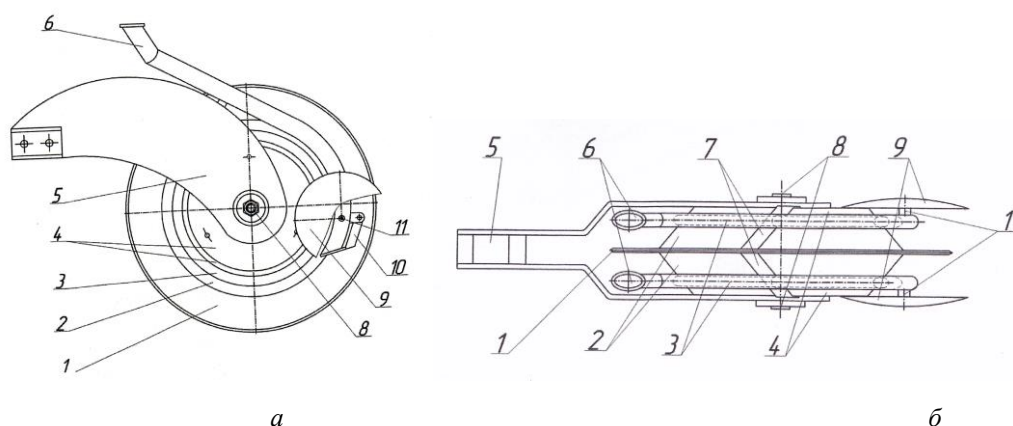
Комбинированный однодисковый сошник с двусторонними ребрами и сферическими дисковыми загортачами для узкорядного посева: а – вид сбоку; б – вид сверху; 1 – плоский диск; 2 и 4 – реборды; 3 – бороздкообразователи; 5 – корпус; 6 – семянаправители; 7 – чистик; 8 – ось; 9 – сферический диск; 10 – клапан; 11 – оси
